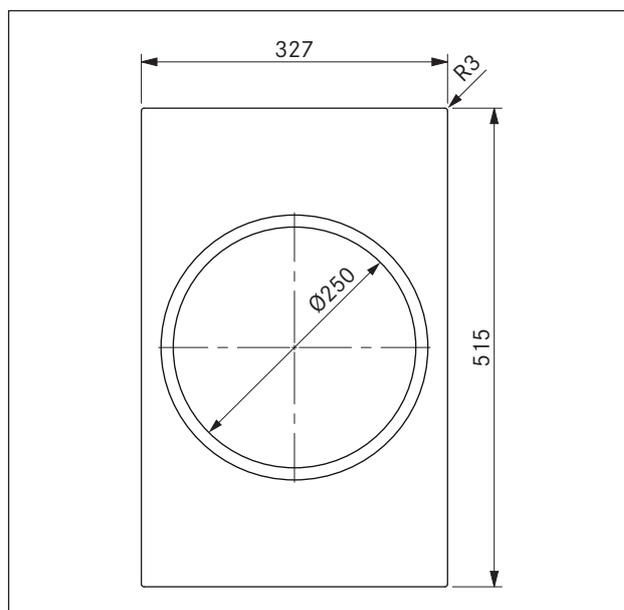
Dimensões do aparelho CKIW, vista de cima
